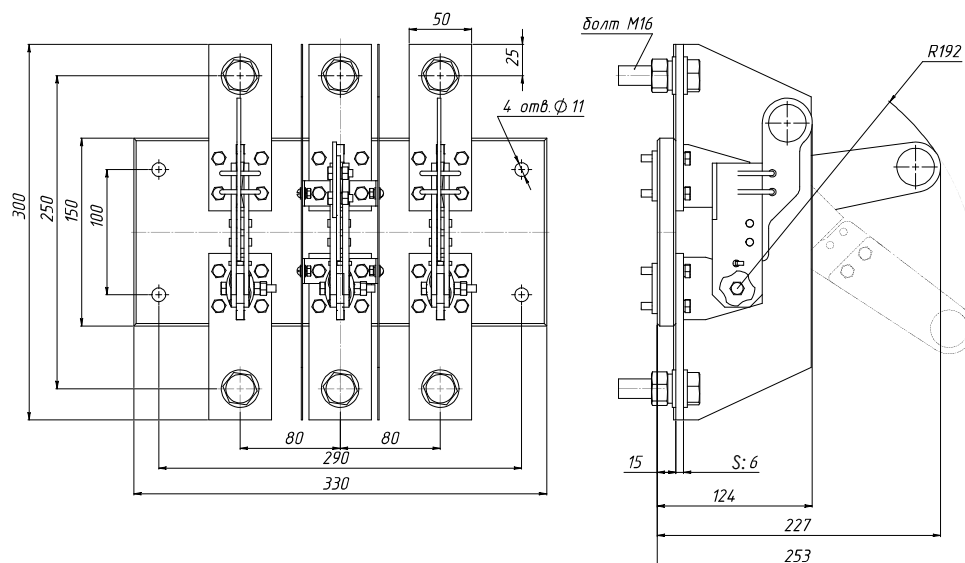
Разъединитель P103 с пополюсным оперированием штангой ШО-1, на номинальный ток 1000 А
